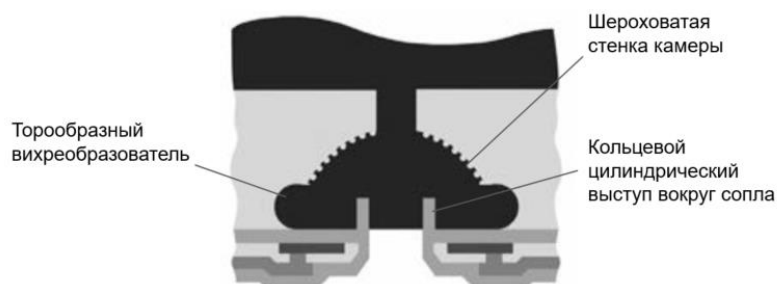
к финальному решению - сделать стенки полусферической камеры и дно шероховатыми
